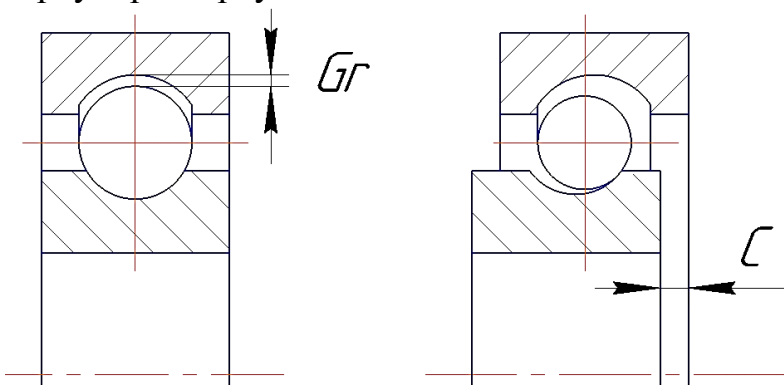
Монтажный и осевой зазоры подшипника
